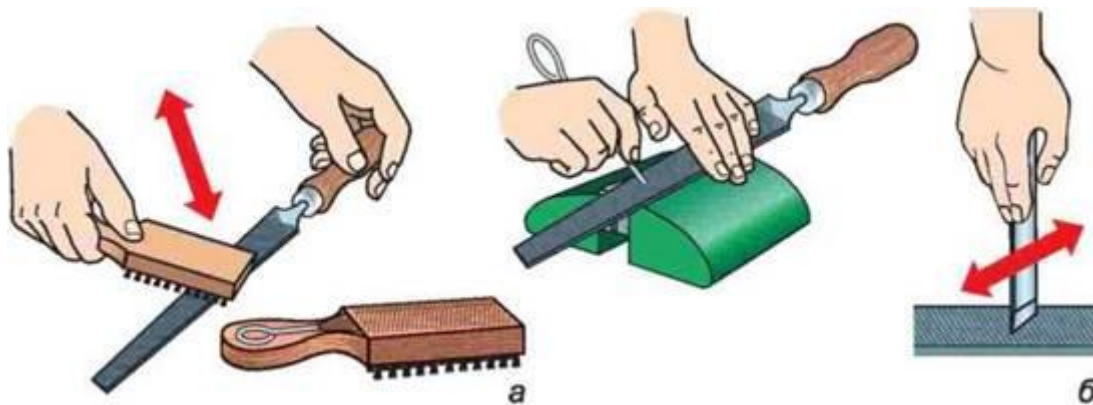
Очищення напилка: а - металевою щіткою; б - шкребками
